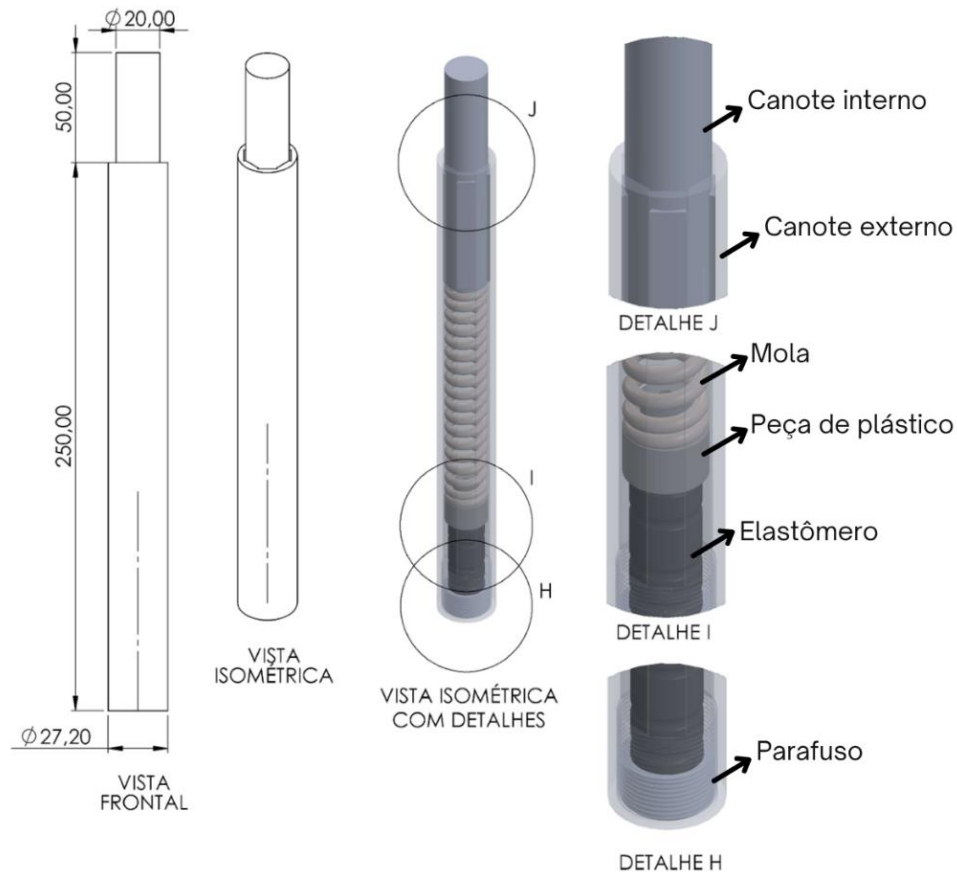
Desenho técnico do canote convencional com amortecimento (em mm)
